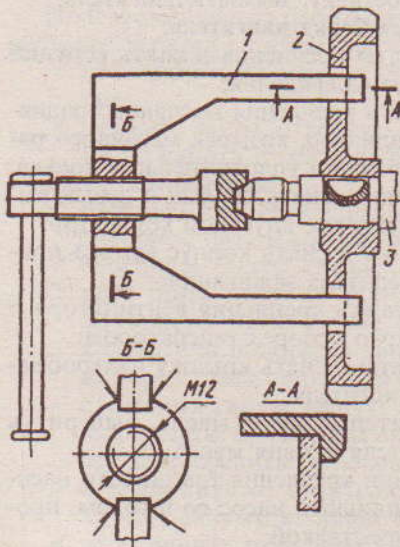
Съемник для снятия шестерни балансирующего вала: 1 – съемник; 2 – шестерня балансирующего вала; 3 – балансирующий вал
